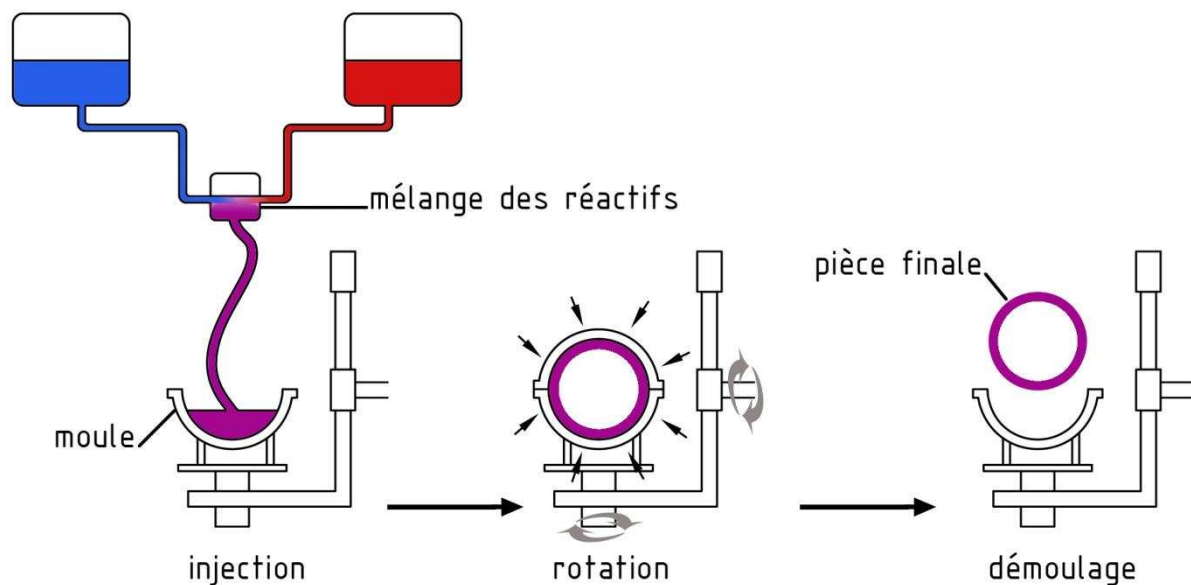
Schéma décrivant le procédé de rotomoulage réactif.
